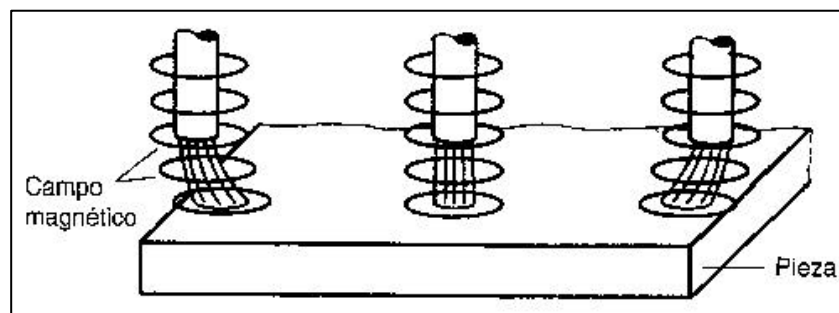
SOPLO MAGNÉTICO AL SOLDAR CERCA DE LOS EXTREMOS DE UNA PIEZA FERROMAGNÉTICA
